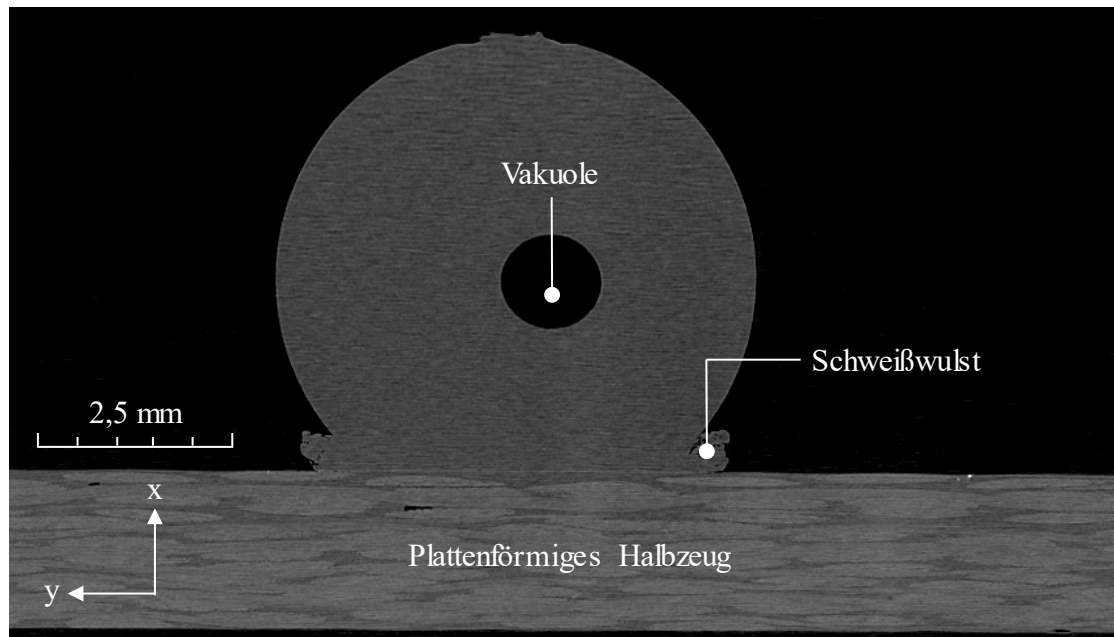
CT-Bild der Schweißverbindung PA6-CF/PA6 [138]
